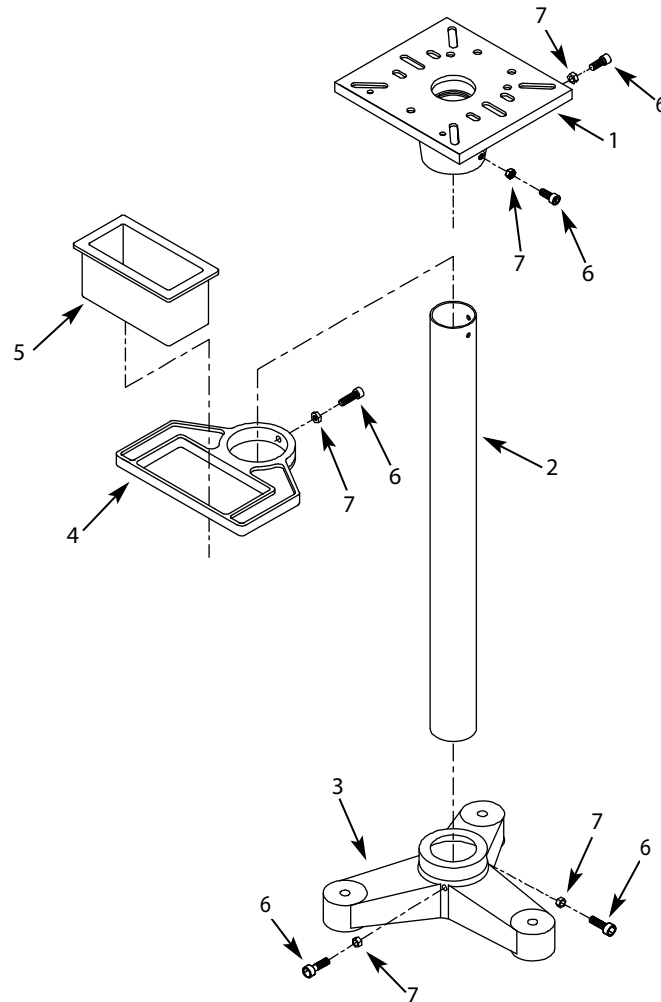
Illustration des pièces de rechange pour le support de la meuleuse d'établi.
